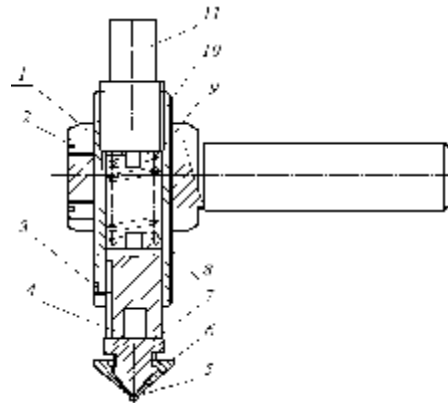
Накатний інструмент: 1 – державка; 2 – гвинт; 3 – обмежувач ходу; 4 – плунжер; 5 – кулька; 6 – ковпачок; 7 – опора; 8 – пружина; 9 – шайба; 10 – корпус; 11 – натяжний гвинт
